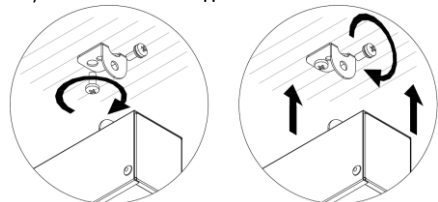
Установка крепления уголок для накладного монтажа.
